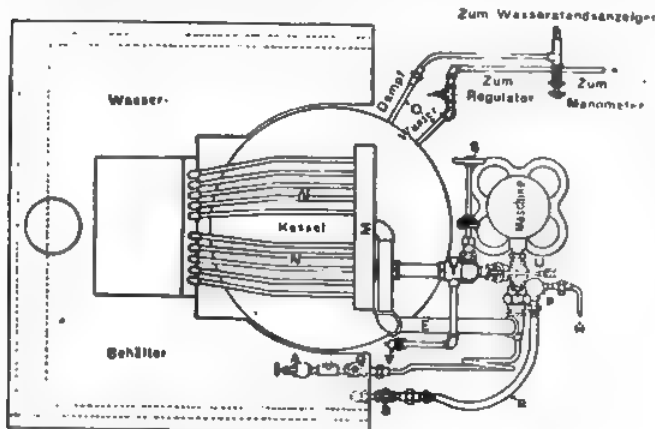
Grundriss der Kessel- und Maschinen-Anordnung.
